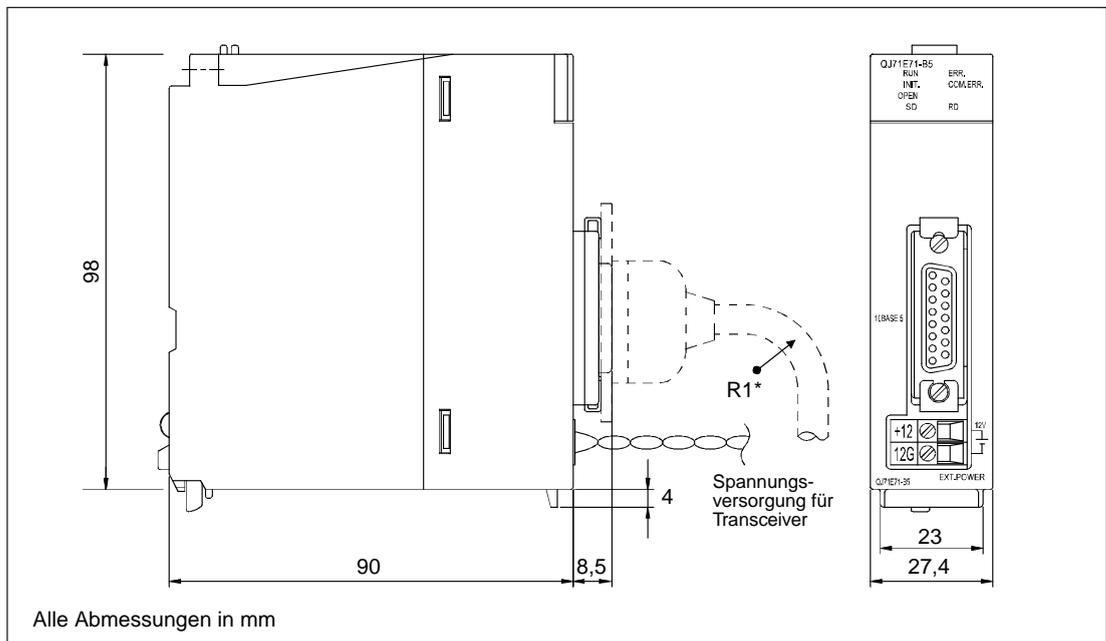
Gehäuseabmessungen des QJ71E71-B5
